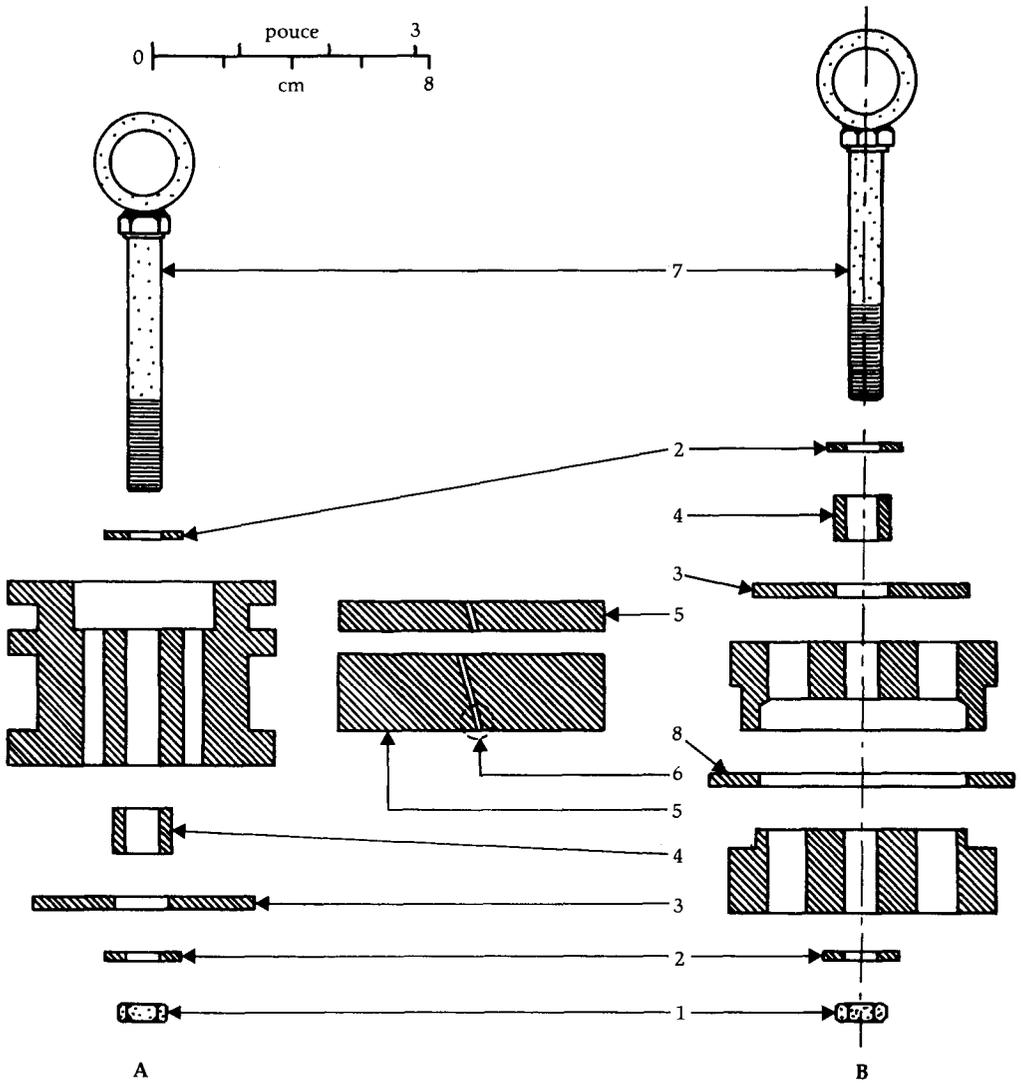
Piston (A) et clapet de pied (B) original : 1) écrou six pans ; 2) rondelle ; 3) capuchon de soupape en plastique ; 4) capuchon de soupape-guide de course ; 5) segment de piston en plastique ; 6) fente en diagonale ; 7) boulon fileté muni d'un joint torique soudé en place ; et 8) joint en caoutchouc.
